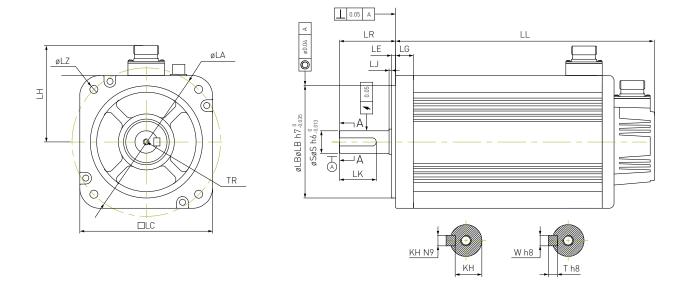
Габаритные размеры серводвигателя ELM2H-xxx (220VAC).
